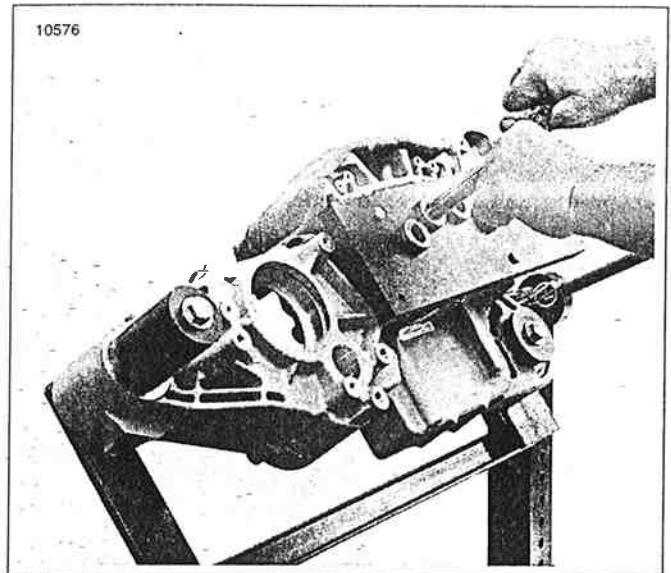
Escariado del buje del engranaje de la leva en la mitad derecha del cárter
